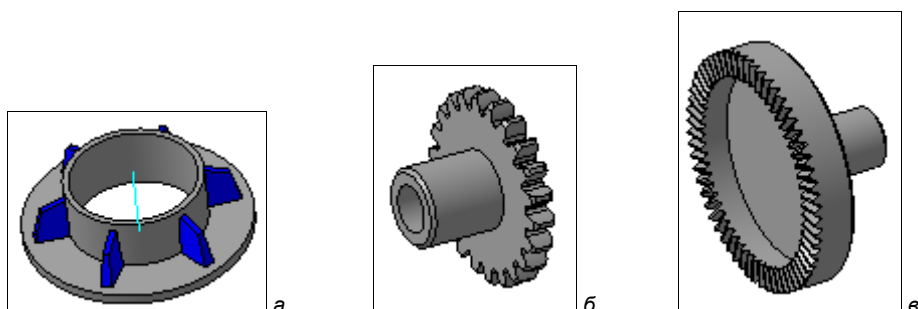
а — Модель 10 с ребрами; б — Зубчатое колесо 22;
